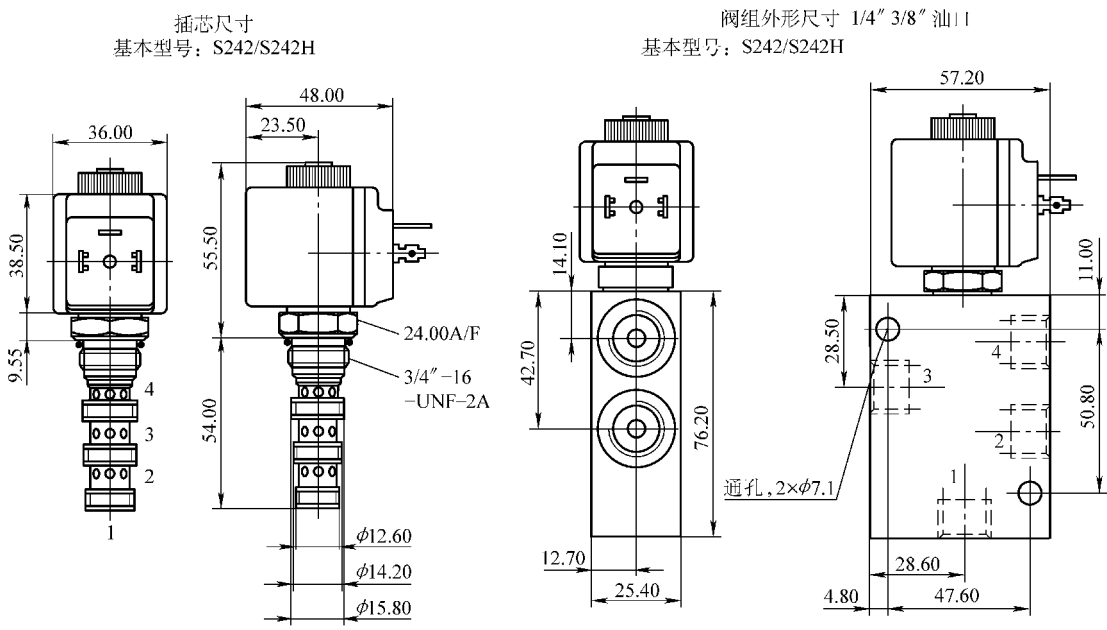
S224/S242H 型电磁换向阀外形尺寸
